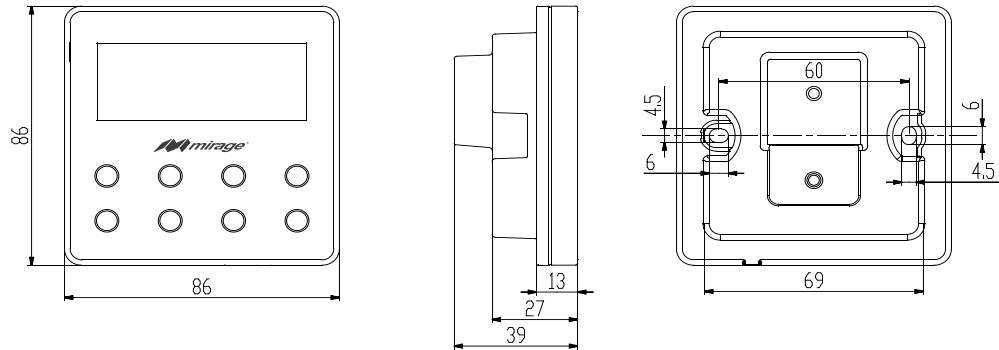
Dimensiones del controlador de zona (Unidades: mm)
